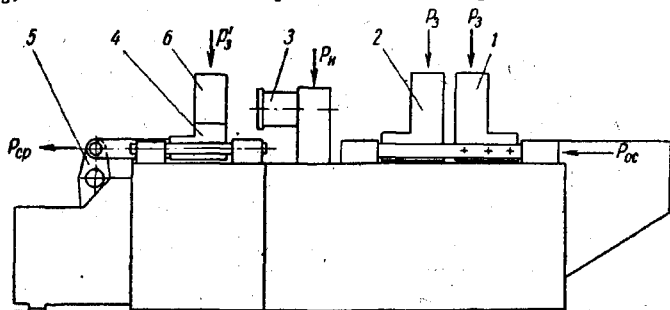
Автоматическая стыковая машина РСКМ-320У с электроприводом для сварки оплавлением с подогревом.
